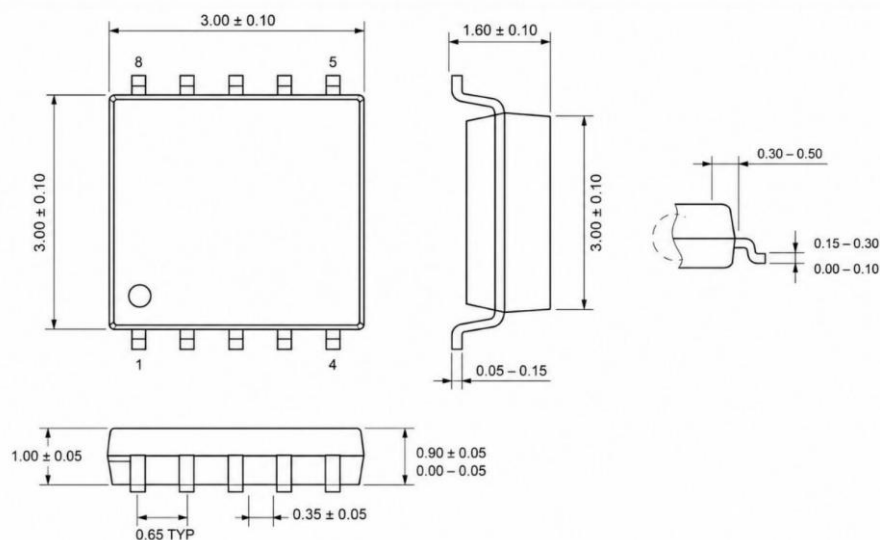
Зовнішній вигляд і розміри корпусу імпульсивного понижувального DC-DC регулятора LMR14030SQDPRRQ1
